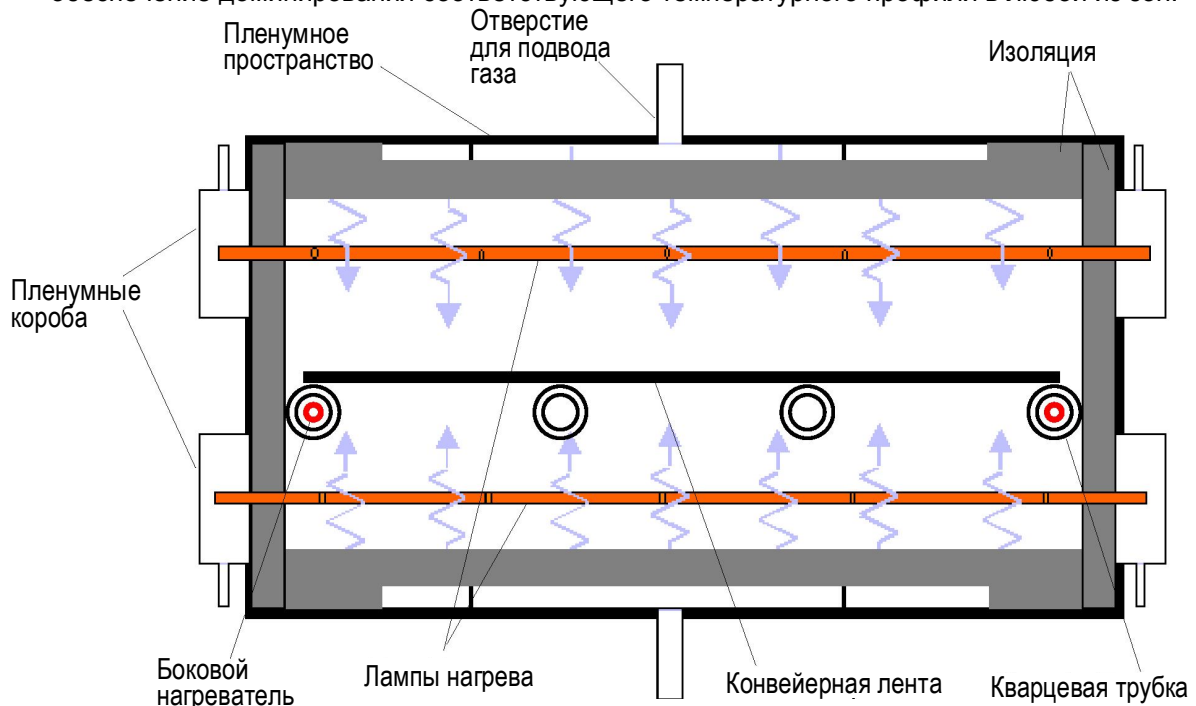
Вид печи в разрезе с отмеченными боковыми нагревателями
